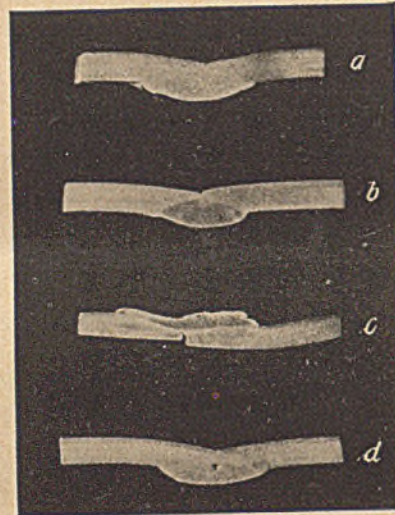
Schnitte durch die Schweißnaht, geätzt.
